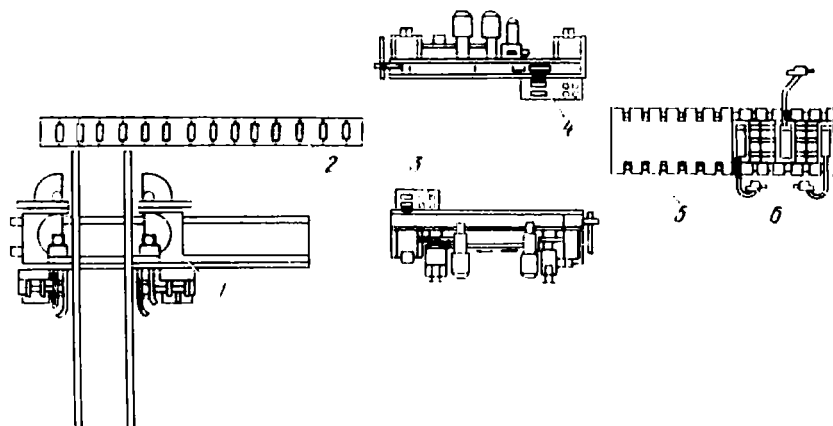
Схема линии нарезания шипов и установки приборов в брусках коробок ДВ205:
